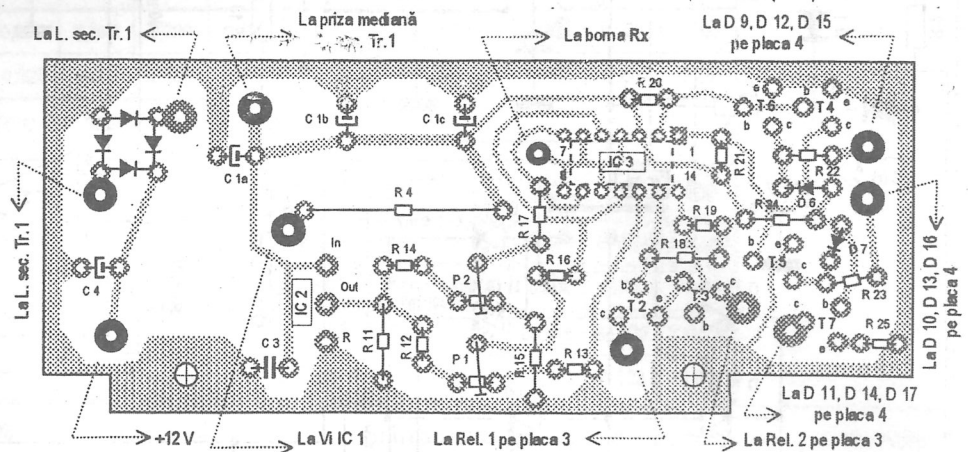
Placa 1; dispunerea componentelor, vedere dinspre fața superioară.
